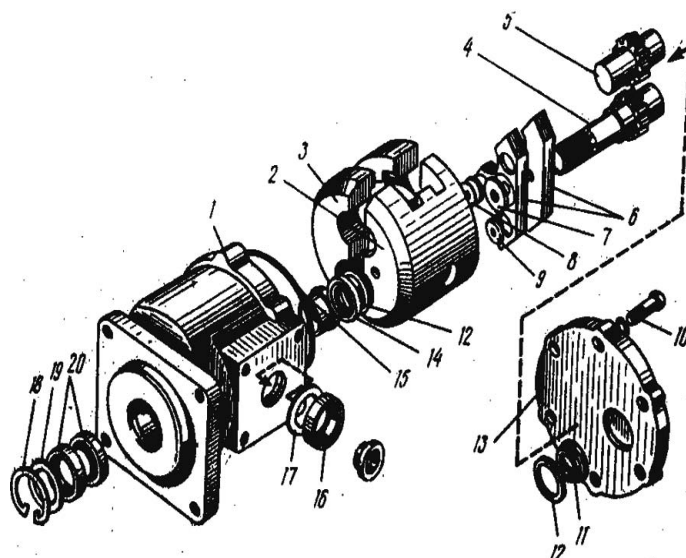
Разборка шестеренного насоса НШ-32-2. 1 — корпус; 2 — поджимная обойма; 3 — подшипниковая обойма; 4 — ведущая шестерня; 5 — ведомая шестерня; 6 — пластики; 7, 9, 11, 14, 16 и 20 — манжеты; 8 — пластина; 10 — болт; 12 — кольцо; 13 — крышка; 15 — уплотнительное кольцо; 17 — опорная пластина; 18 — пружинное упорное кольцо; 19 — опорное кольцо
